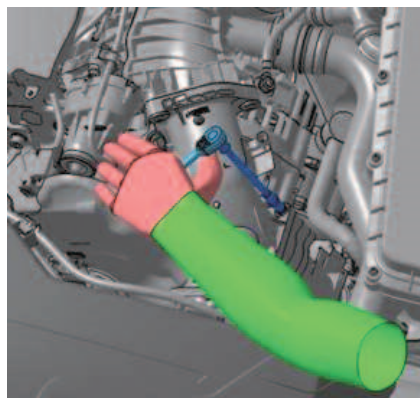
Es wird geprüft, ob das Werkzeug (blau) an der Schraube platziert werden kann. Der Mensch benötigt Platz zur Bedienung des Werkzeugs (3D-Arm)
